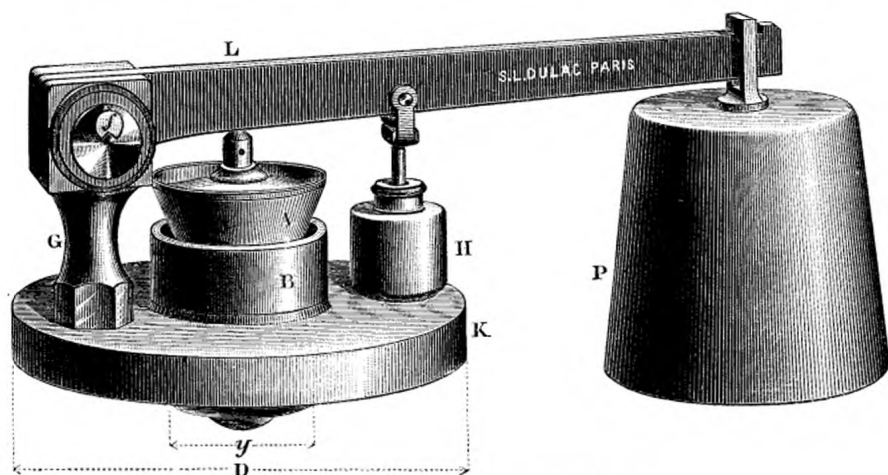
VUE PERSPECTIVE D'UNE SOUPAPE.
